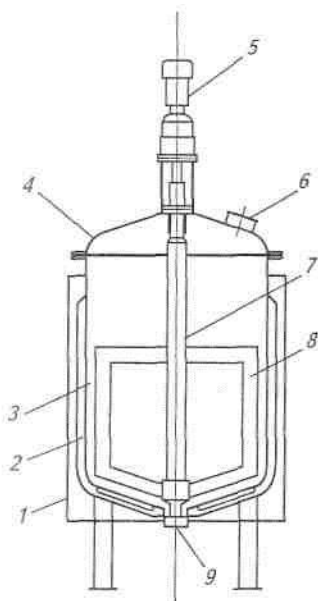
Схема сироповарочного котла: 1 - обечайка; 2 - теплообменная рубашка; 3 - цилиндрический сосуд; 4 - цилиндрический сосуд; 5 - привод; 6 - загрузочный люк; 7 - вал мешалки; 8 - мешалка; 9 - разгрузочный люк.
